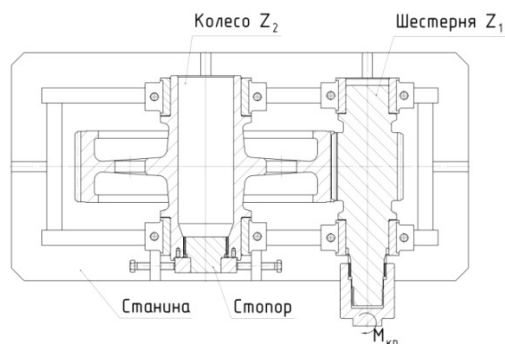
Принципиальная схема установка статического нагружения шестерни z_1 и колеса z_2 первой ступени опытного энергетического редуктора
